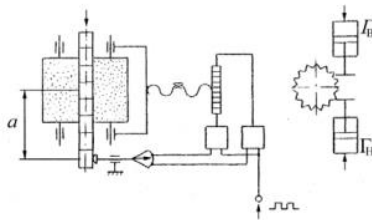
Схема обробки на безцентрово-шліфувальному верстаті з трьохпозиційним регулятором
